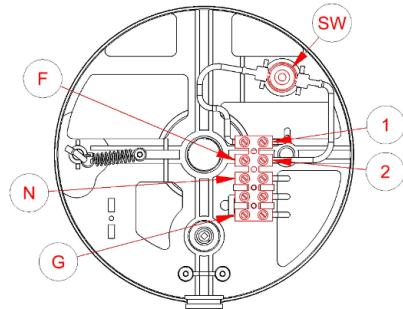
2 KABEL + Thermoschutzschalter
